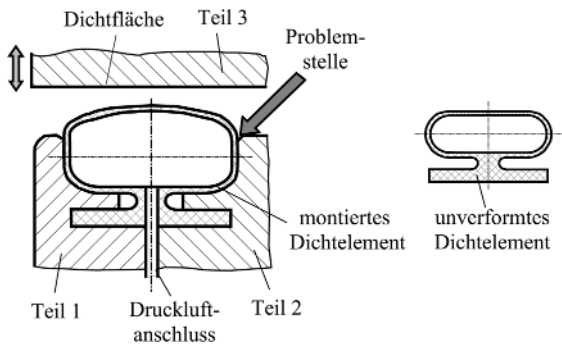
Prinzipbeispiel einer Dichtung mit Druckbeaufschlagung.
